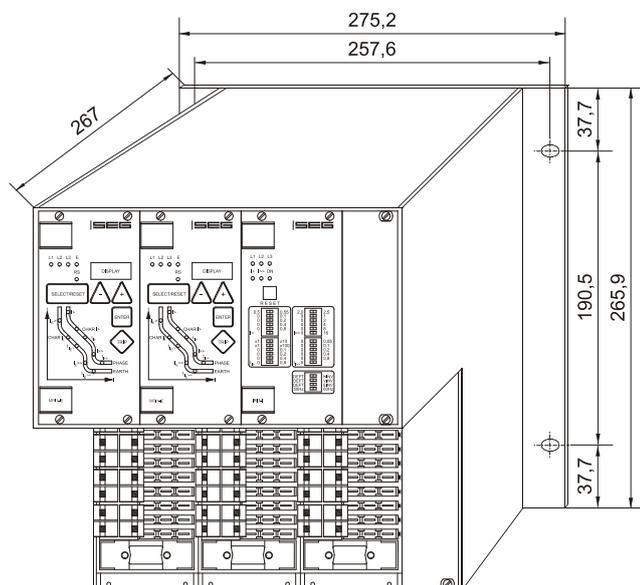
Baugruppenträger für Montageplattenaufbau mit Relaisvariante A, 42 TE
